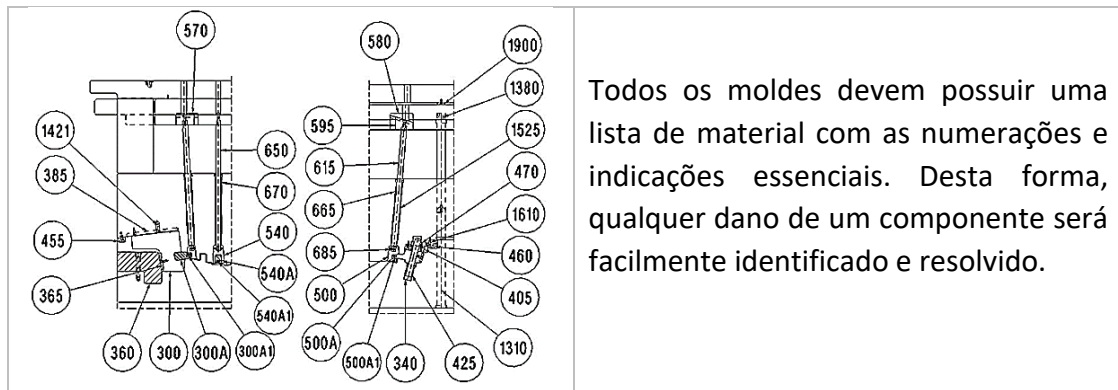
Desenho 2D de um molde completamente estruturado e referenciado (Grupo Simoldes, 2016)
